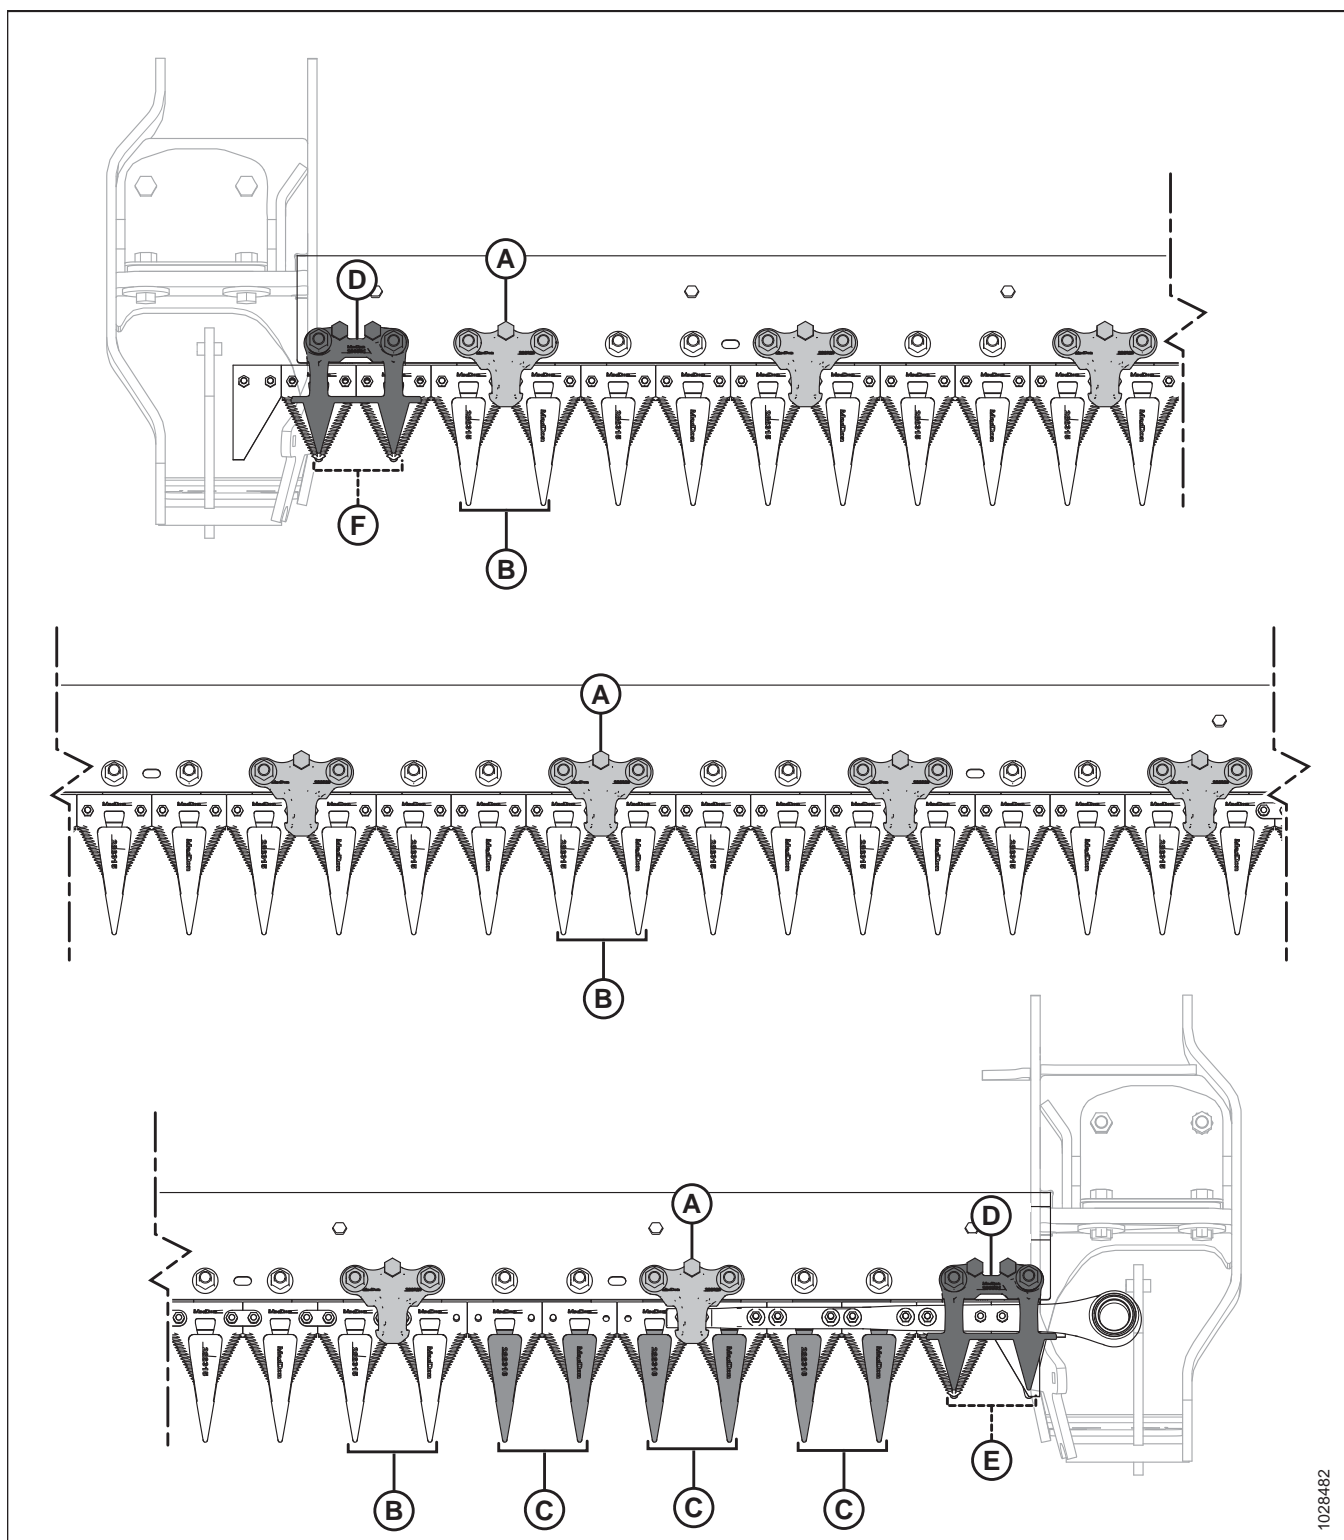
Местоположение заостренных противорезущих пальцев и прижимов — жатки с одинарными ножами
